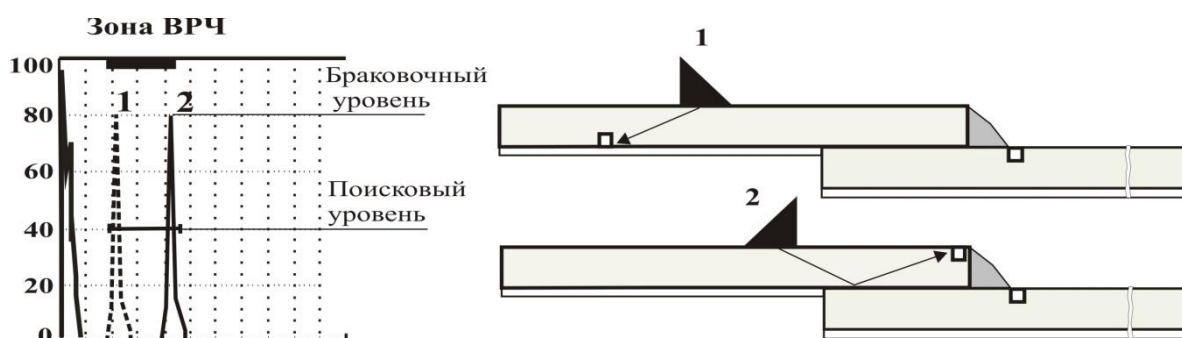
Схема настройки чувствительности при контроле нахлесточных сварных соединений труб со стороны верхнего элемента
